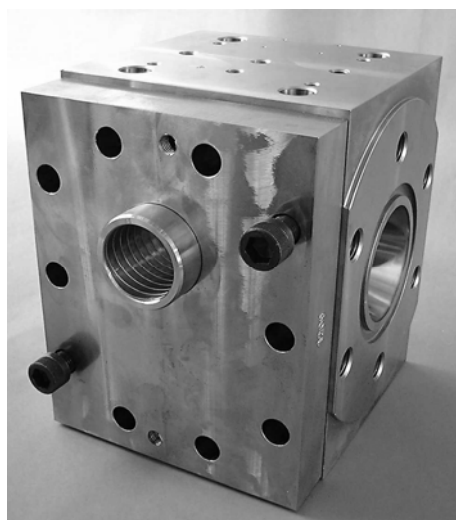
Привинчивание крышки стороны, противоположной приводу
